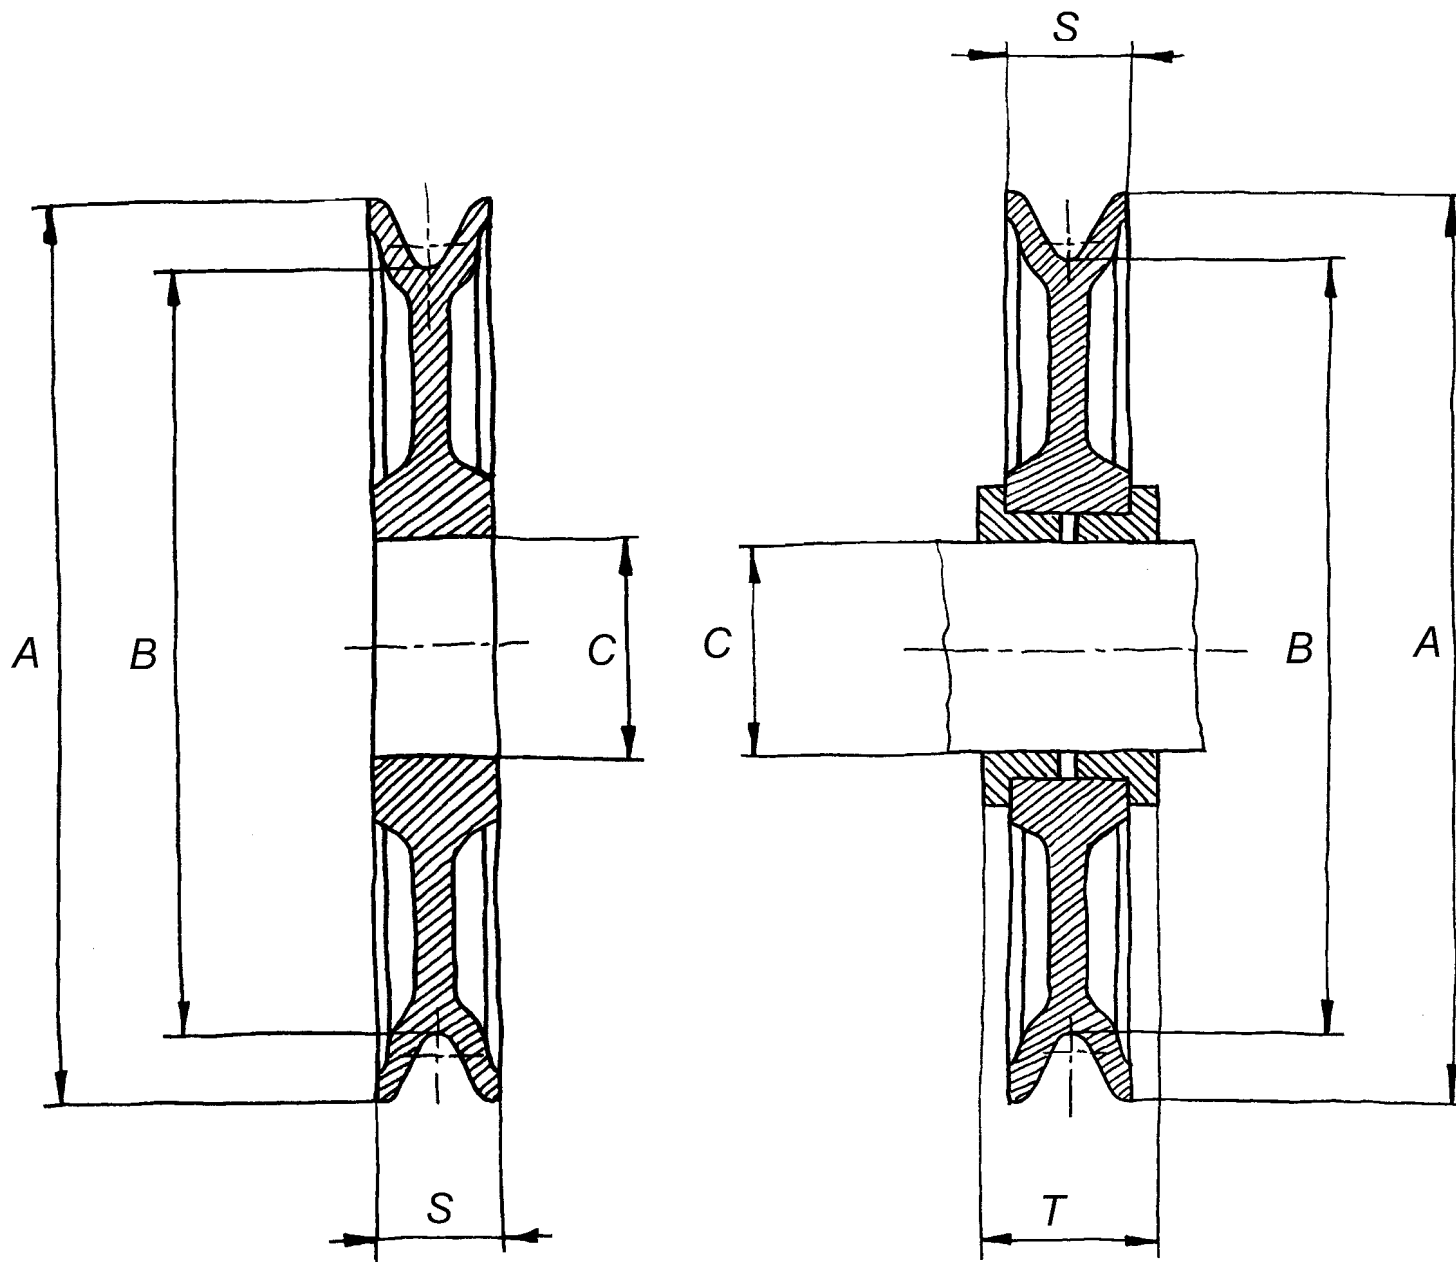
Dimensioni principali carrucola (a) senza e (b) con boccole flangiate in bronzo.
